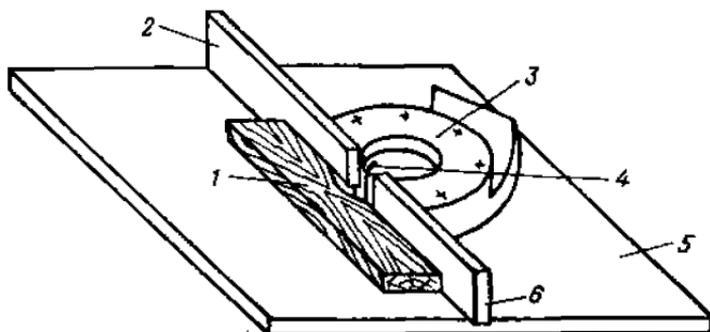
Сквозное фрезерование прямолинейных деталей по линейке
